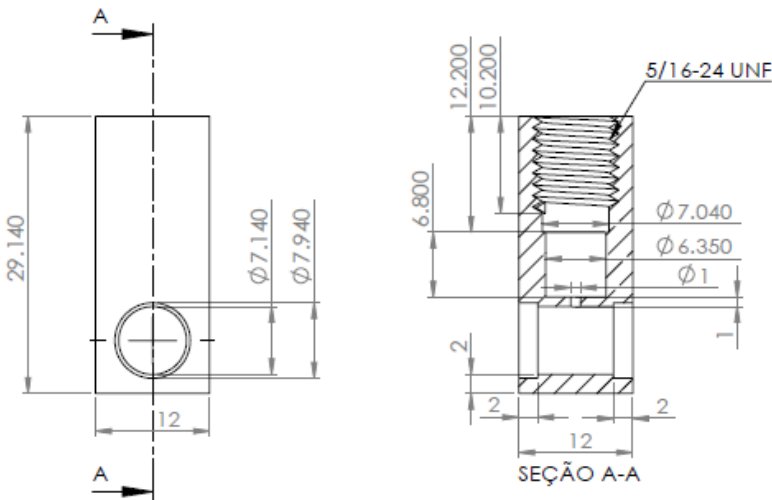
Desenho do alojador do evaporador (dimensões em [mm]).
